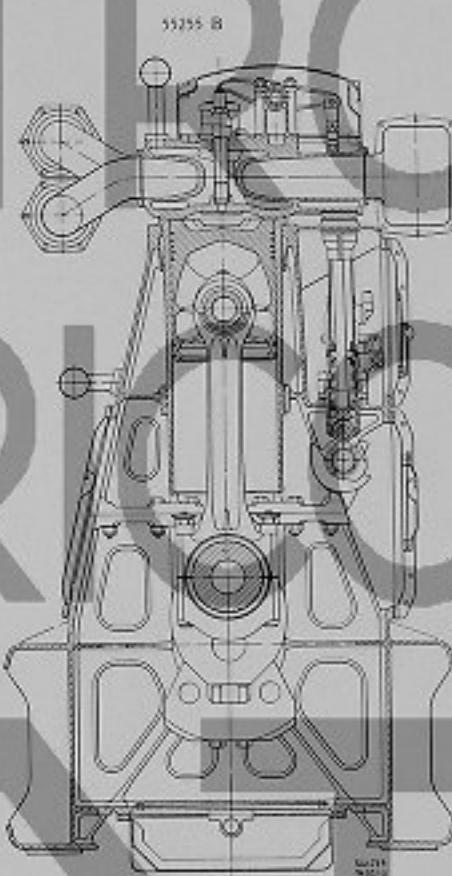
Sezione trasversale del motore SULZER tipo 8 LDA 28
